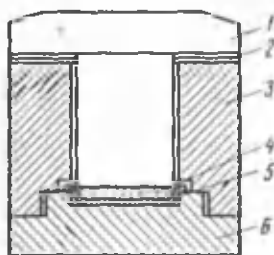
Прессформа для запрессовки цинкового порошка в крышку ртутно-цинкового элемента:
